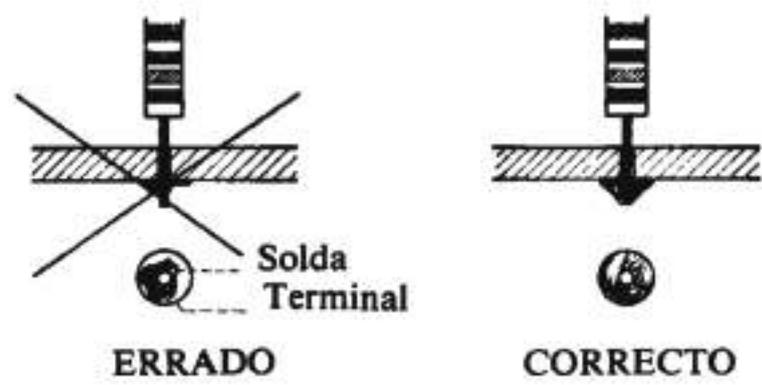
Exemplo correto e incorreto de solda em PCI.
